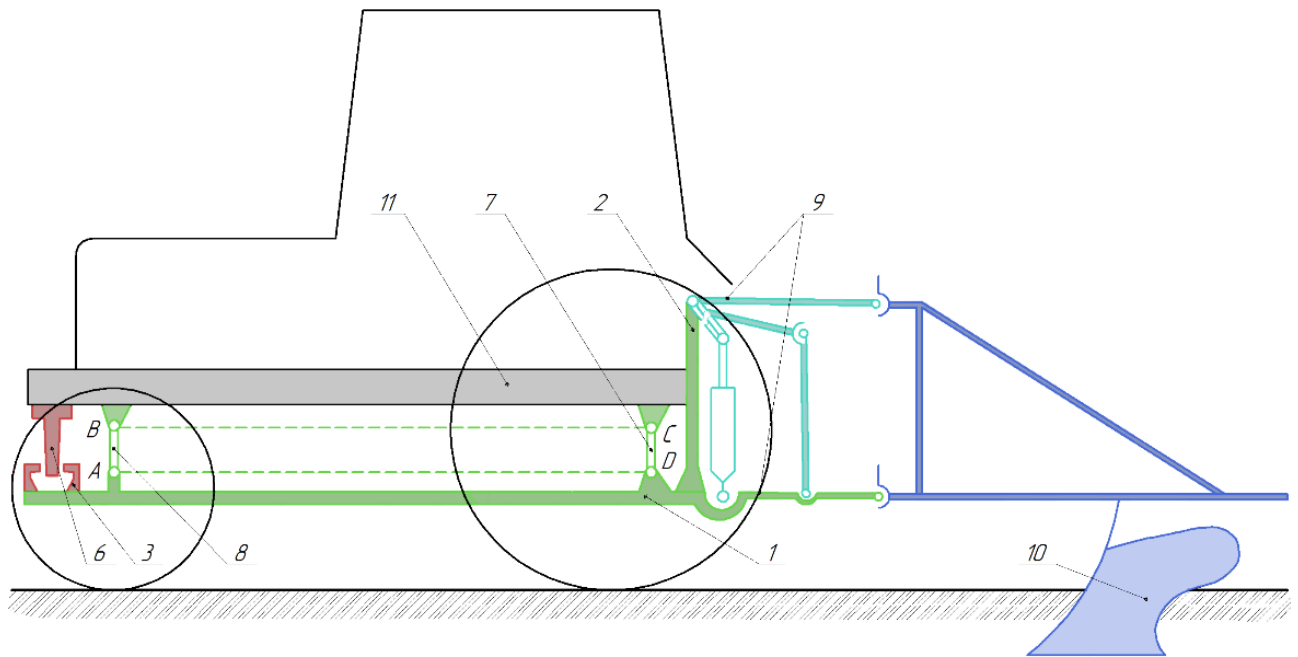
Кінематична схема пристрою для вимірювання тягового опору машини (для тракторів традиційного (класичного) компоновання): 1 – несуча рама; 2 – кронштейни циліндрів; 3 – тягово-зчіпний механізм; 6 – первинний вимірювальний перетворювач консольного типу; 7 – задній маятниковий вузол; 8 – передній маятниковий вузол; 9 – задній навісний пристрій; 10 – машина – знаряддя; 11 – рама трактора задня [1, 5, 8].
